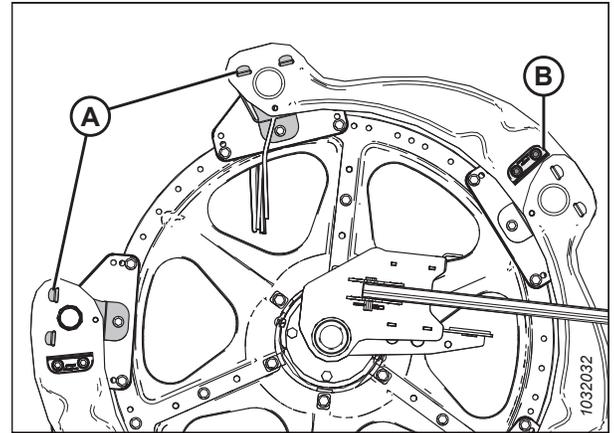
Bouclier du rabatteur enlevé - Extrémité arrière extérieure
